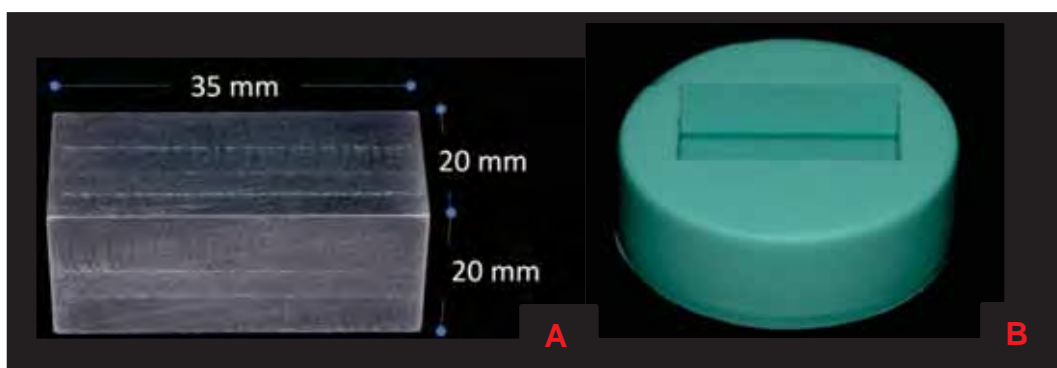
A-B - A) Padrão em alumínio; B) Molde de silicona de adição.
